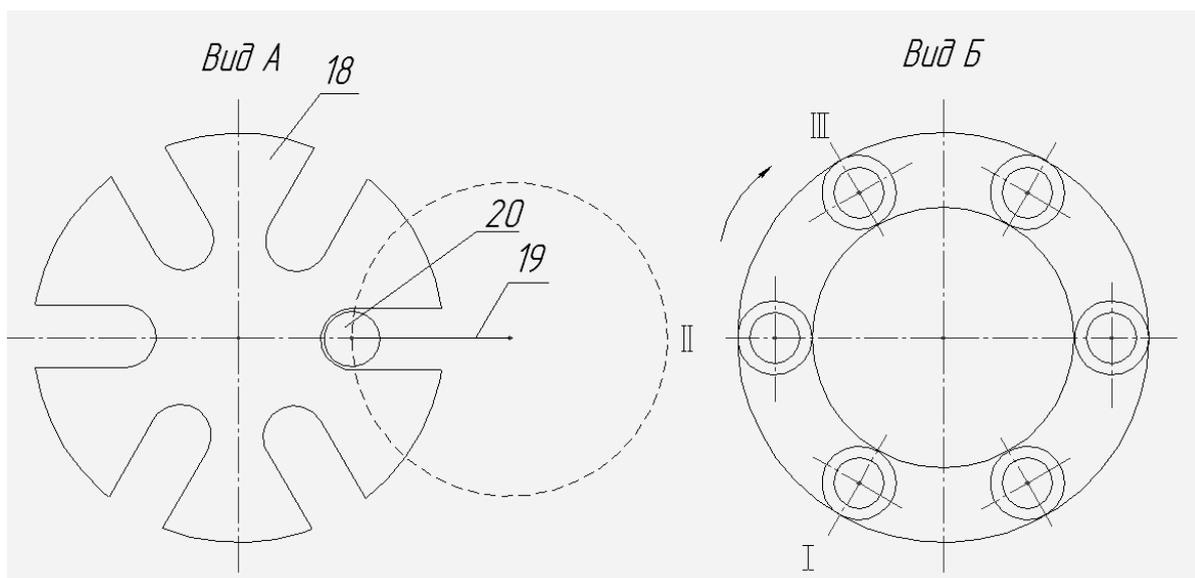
Вид А – мальтийский крест; Вид Б – револьверный диск (кассеты условно сняты).
